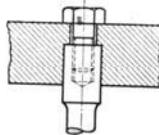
Stempelbefestigung durch Haftsitz und Zugschraube.
